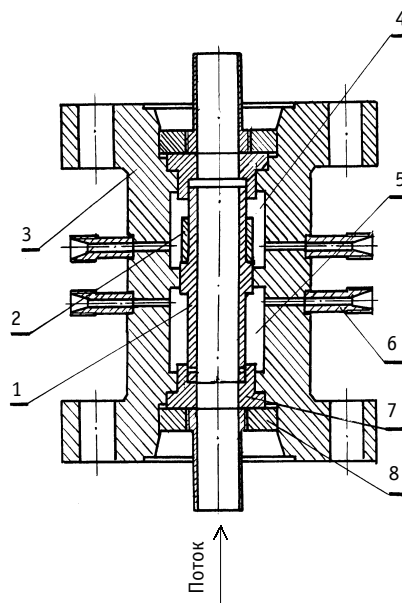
Конструкция устройства для измерения касательных напряжений (τ -метра): 1 – подвижный элемент трубы; 2 – грузик; 3 – корпус; 4 – камера верхняя; 5 – камера нижняя; 6 – штуцеры подсоединительные; 7 – направляющая; 8 – кольцо запорное
